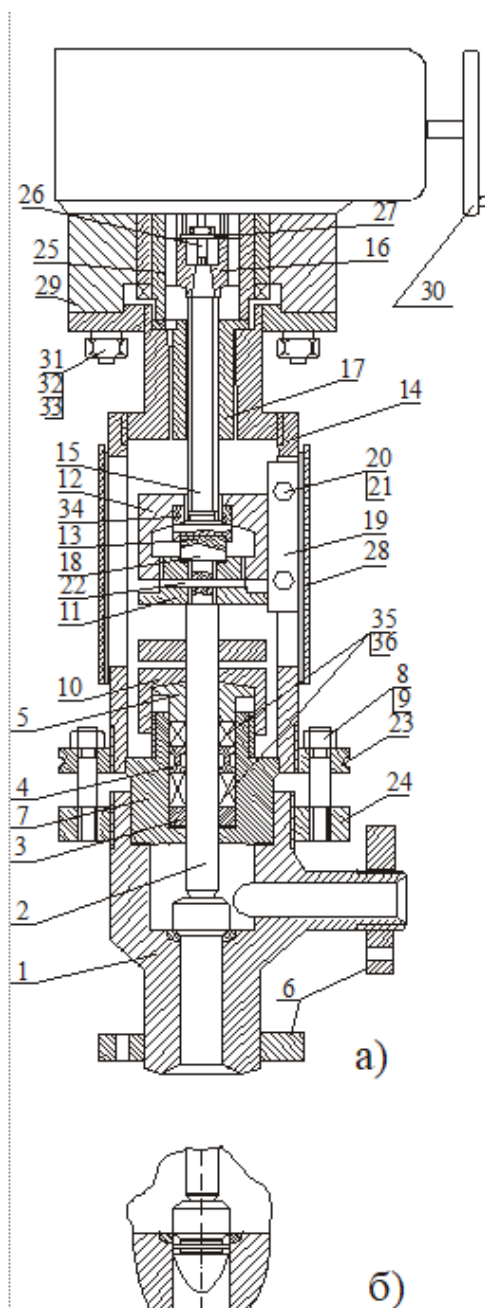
Конструкція запірною АК 23031 (а) і вузол затвору запірно-регулюючого АК28016 (б) клапану для Ду50 фланцевого виконання: 1 - корпус; 2 - шток; 3 - кільце опірне; 4 - кільце; 5 - втулка сальника; 6 - фланець з'єднувальний; 7 - корпус сальника; 8 - гайка М24х2; 9 - шпилька М24х2х140; 10 - гайка накладна; 11 - диск; 12 - напівмуфта; 13 - підп'ятник; 14 - стійка; 15 -
